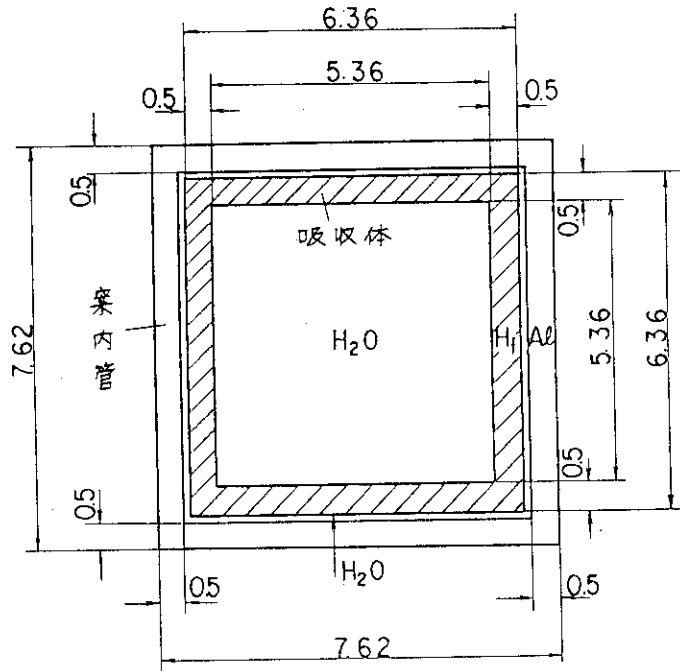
4 制御棒要素水平断面図 (単位: cm)
